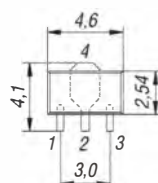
Pinbelegung und Abmessungen (SOT-89)
